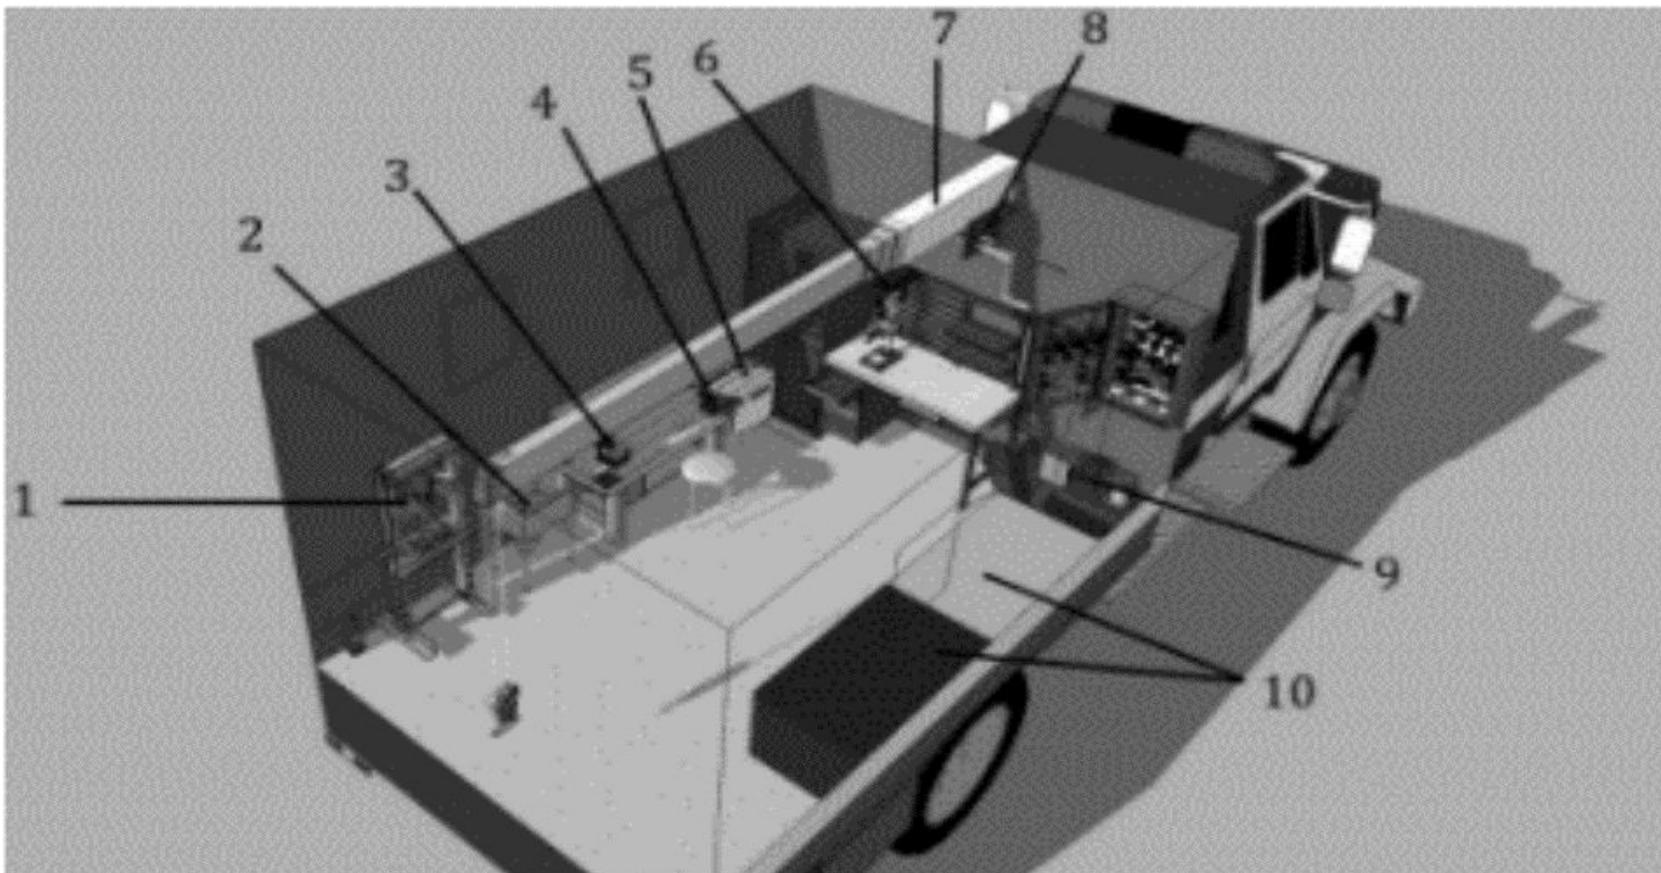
Модель рабочего пространства с расположением оборудования передвижной мастерской: 1 – пресс гидравлический, 2 – мойка, 3 – станок заточной, 4 – тиски, 5 – сварочный аппарат, 6 – сверлильный станок, 7 – грузовая стрела, 8 – редуктор, 9 – компрессор, 10 – рундук
